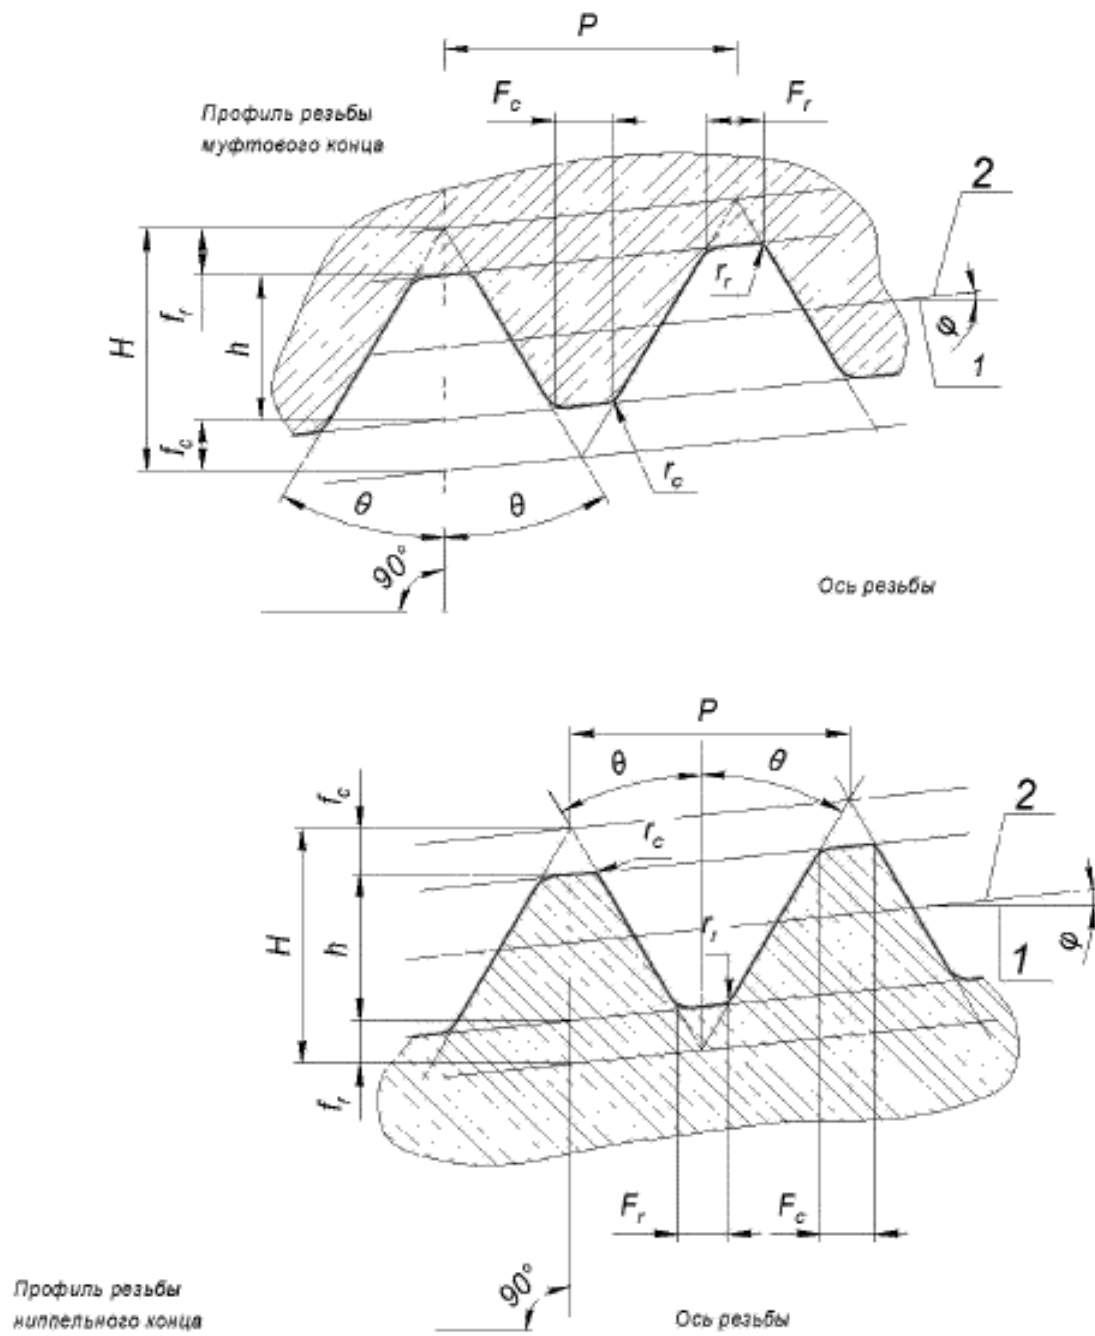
Профиль резьбы V-038R, V-040, V-050
